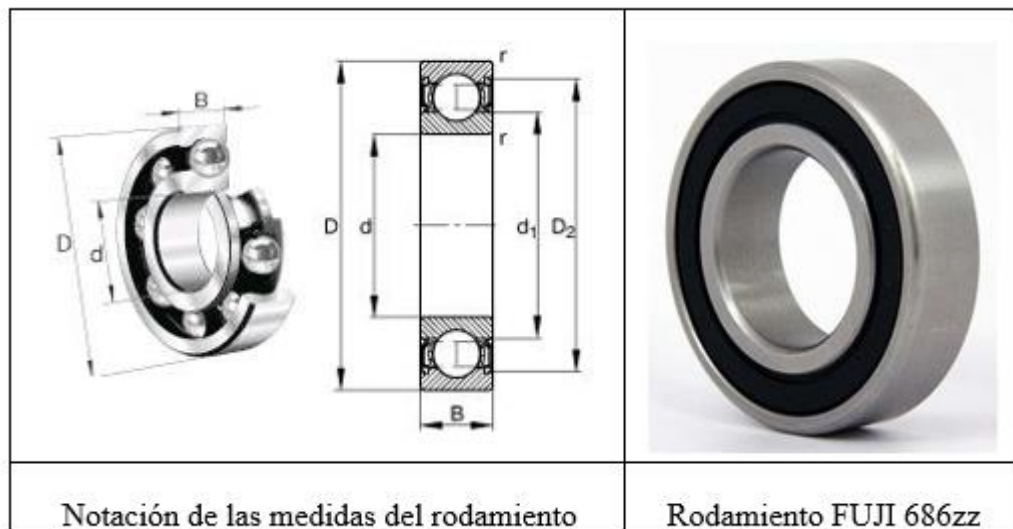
Dimensiones del rodamiento FUJI 686z
